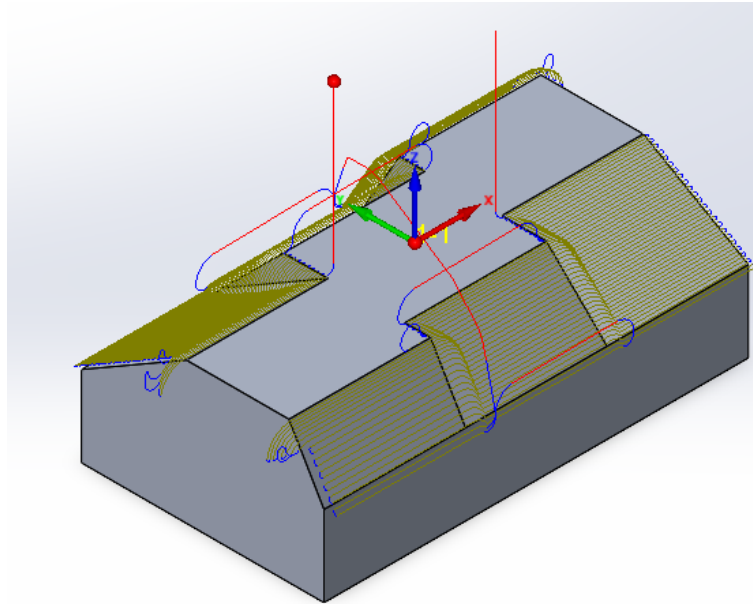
Trajetória executada durante a operação de maquinagem linear
